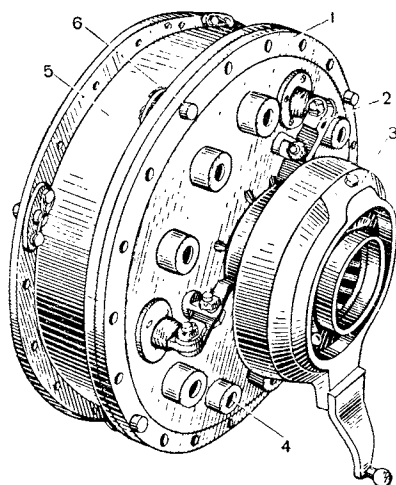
Главный фрикцион (общий вид со стороны двигателя):
